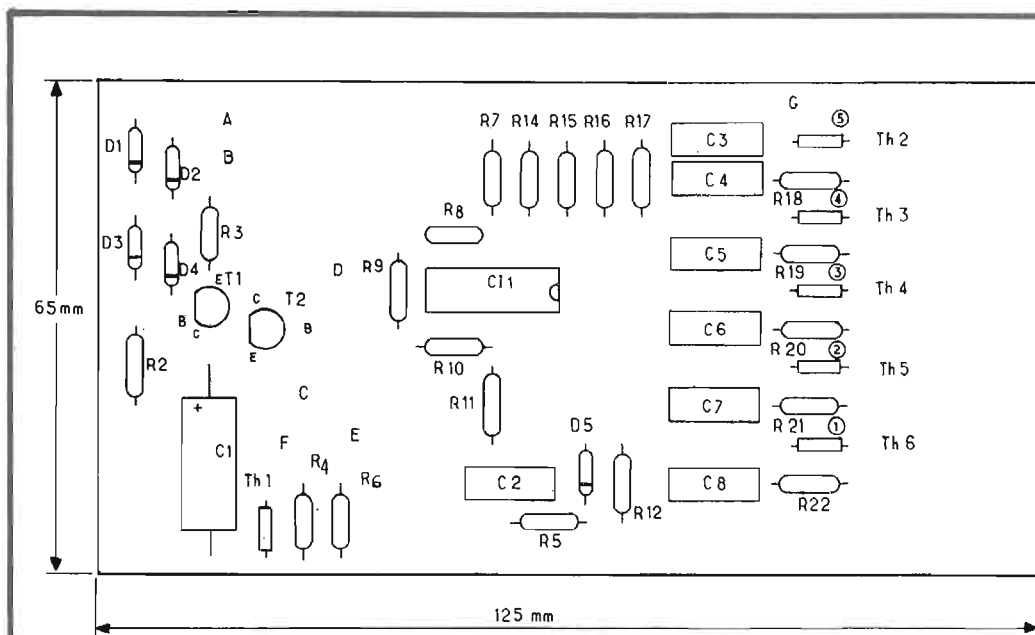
Plan d'implantation des composants, les dimensions destinent cette plaquette à son installation dans une boîte Teko P₄.
